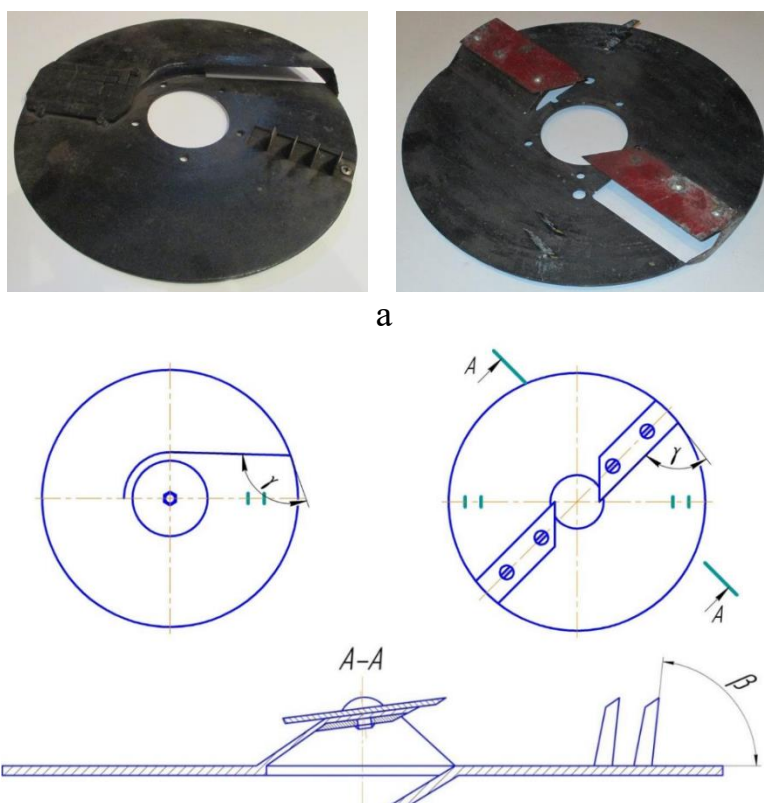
Ріжучі диски з одним і двома горизонтальними ножами: а – фото; б – схема розташування горизонтальних ножів.
